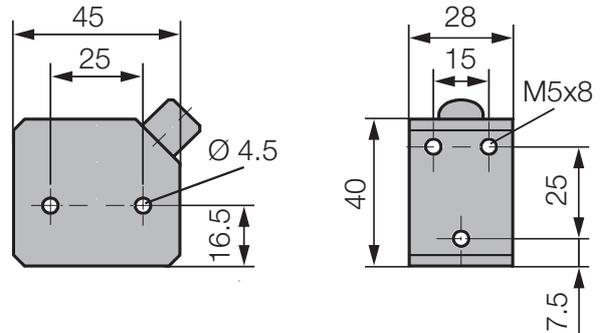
Medidas de montaje del sensor de posición BTL5-P-4500-1
